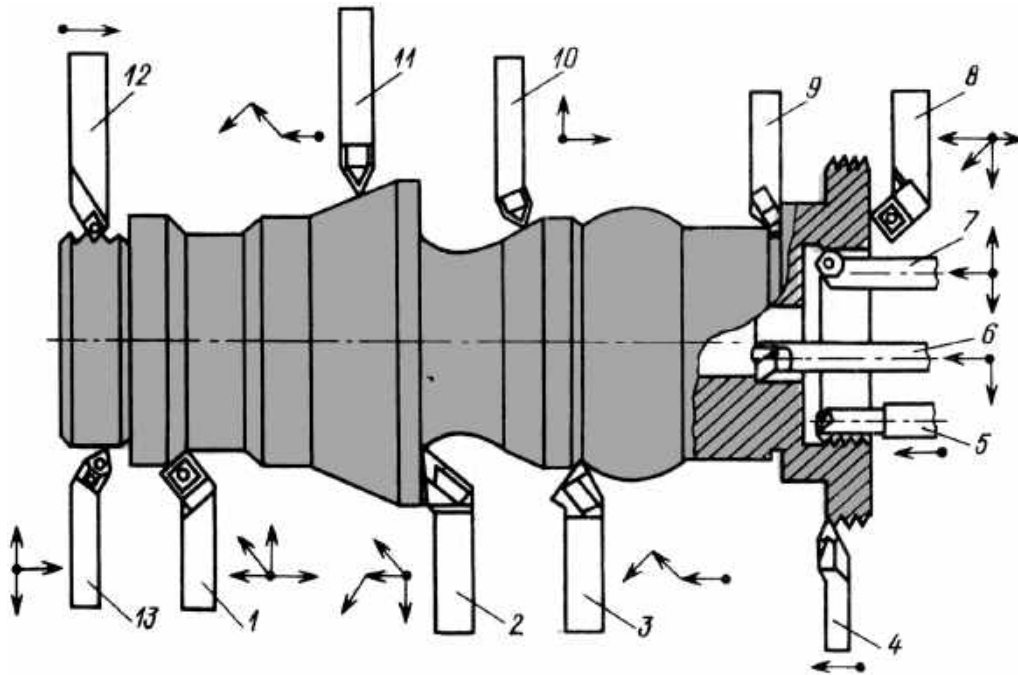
Схема оброблення основних типових поверхонь токарними різцями з БРП
